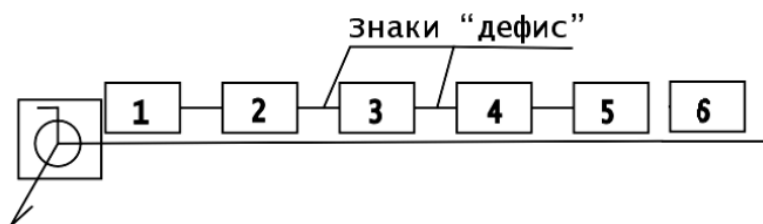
Структура условного обозначения сварного шва
